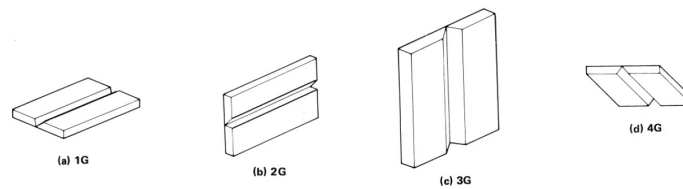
POSICIONES DE PLACAS PARA SOLDADURA DE CANAL.
